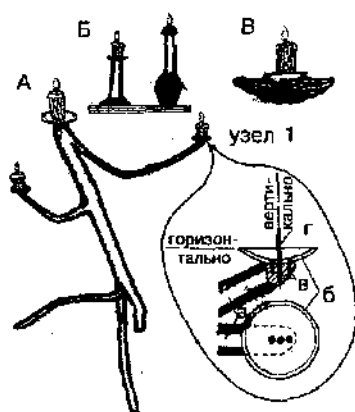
Подсвечники: А — торшер; Б — настольные (канделябры) из ветки с наростом; В — настенный (бра) из трутовика. Узел 1. Крепление деталей: а — основа; б — чашечка; в — шурупы; г — игла
